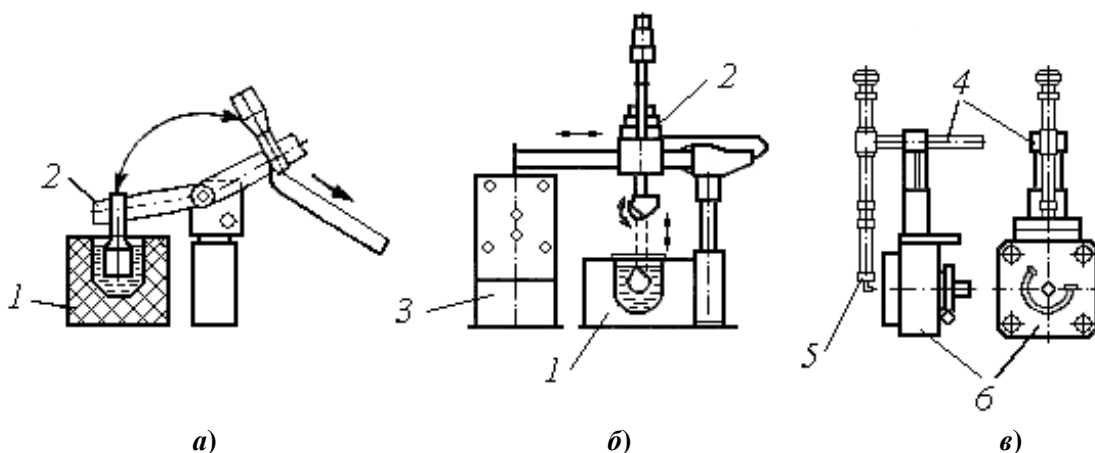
Схемы дозатора-опрокидывателя (а), дозатора портального типа (б) и манипулятора для смазки литьевой формы (в):
